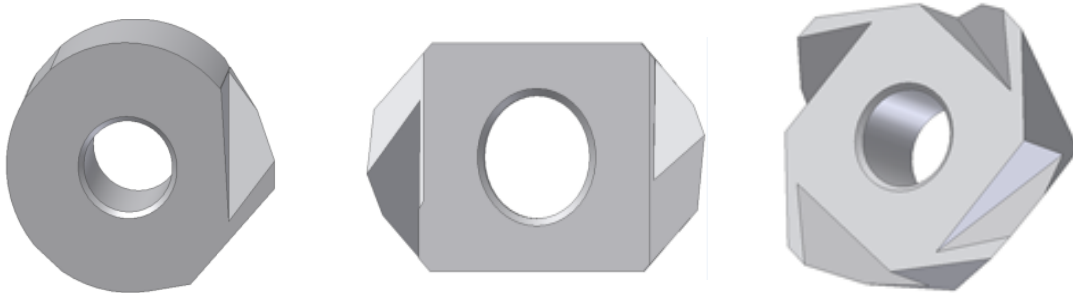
Одно-, двух- и четырехвершинный инструмент ДР для внутреннего поперечного оребрения
